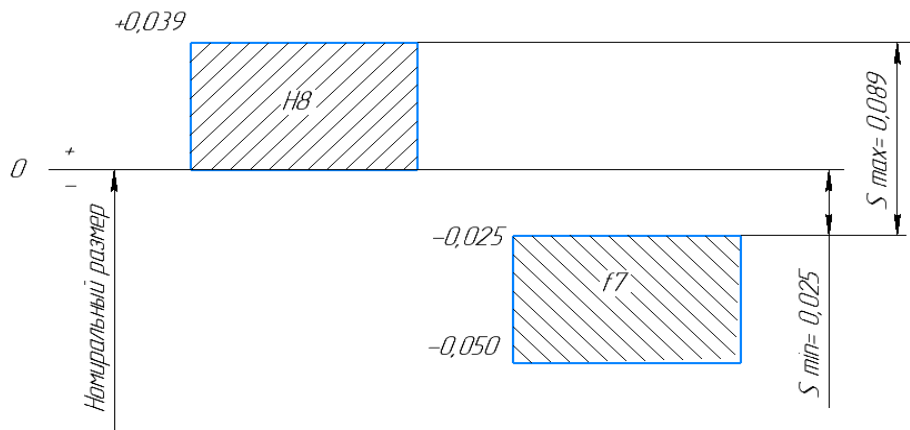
Схема расположения полей допусков посадки с зазором
